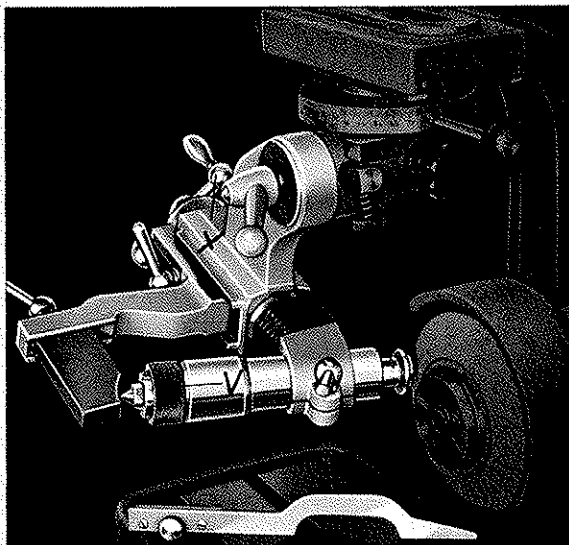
Kopier-Abrichteinrichtung mit Mittenlineal
